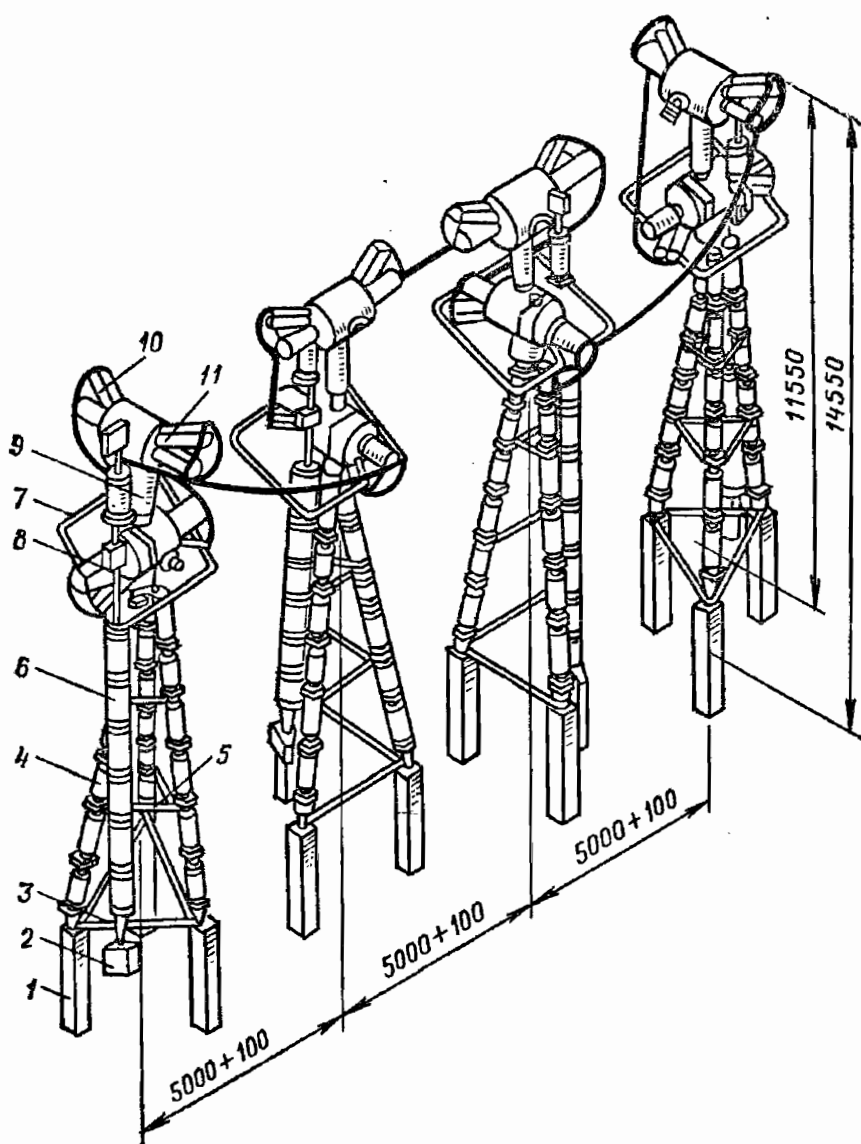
Полюс воздушного выключателя ВВБ-750:
